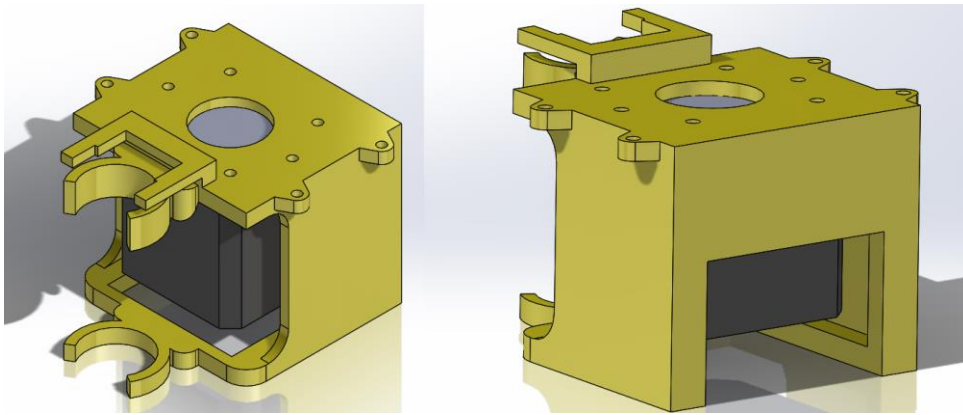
Detalhe do posicionamento do motor na parte inferior do cabeçote
